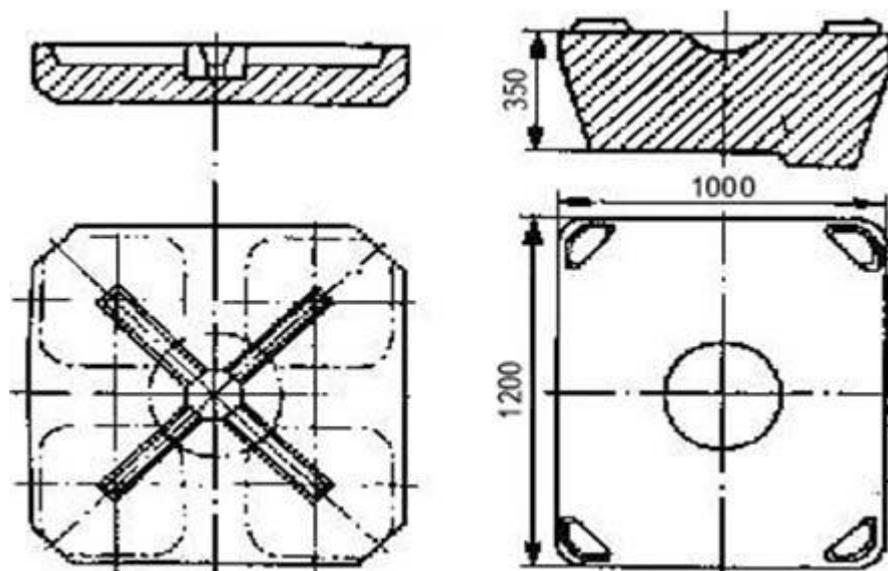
Четырёхместный поддон для сифонной разливки стали (слева), одноместный поддон для разливки сверху (справа)
